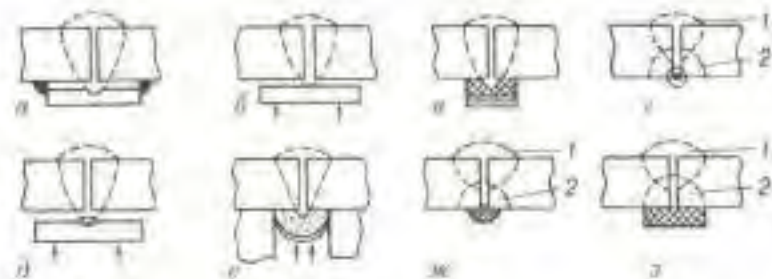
Схеми пристроїв для утримування зварювальної ванни та шлаку й формування зворотного валика при зварюванні під флюсом:
